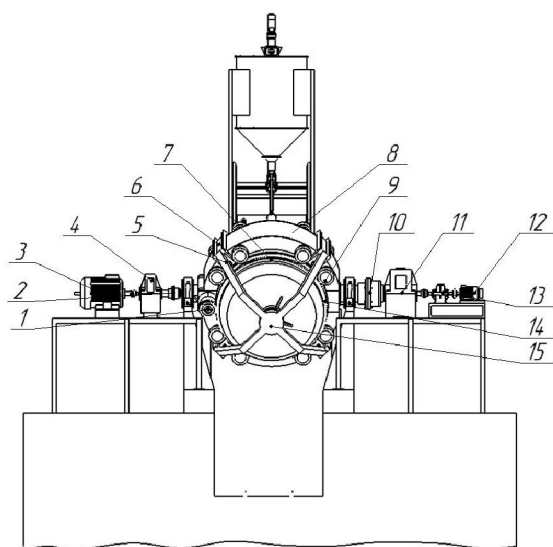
Схема компоновки механизмов наклона и поворота 10-тонного кислородного конвертера конструкции ДонГТУ
